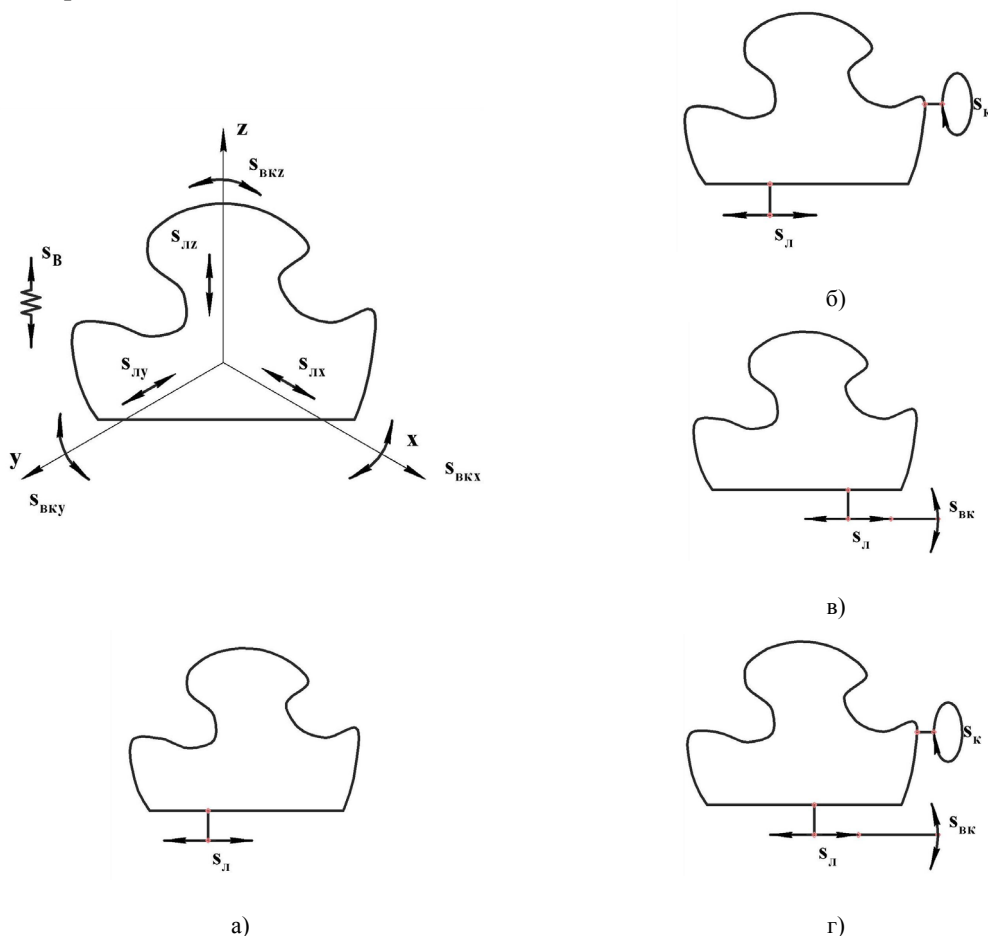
Складнопросторова віброабразивна обробка великогабаритних деталей складної конфігурації та можливі схеми їх примусового руху: а — зворотно-поступального (однокоординатна); б — зворотно-поступального і обертального (двокоординатна); в) зворотно-поступального і зворотно-обертального (двокоординатна); г) додатково до схеми на рис. 4в забезпечується обертальний рух навколо однієї з осей
